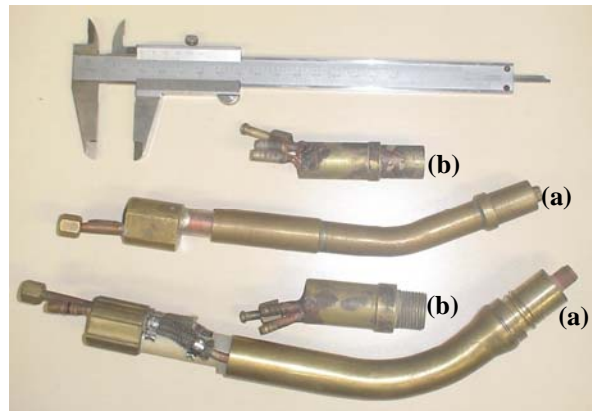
Tocha de soldagem refrigerada a água: (a) encontrada no mercado e (b) projetada.
